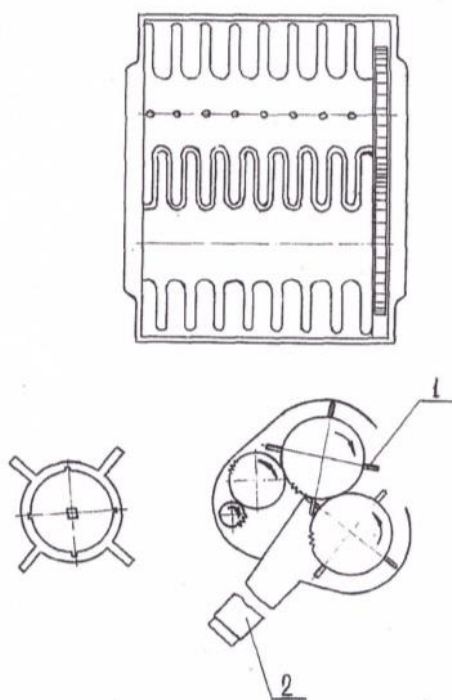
Комбинированное пневматическое устройство для сбора ягод
